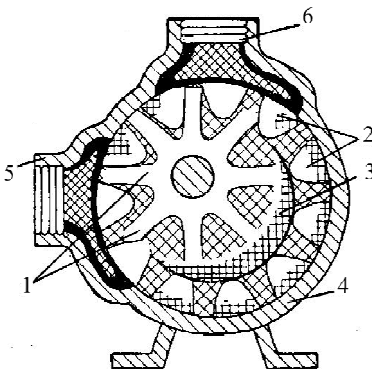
Роторный зубчатый насос с внутренним зацеплением:
